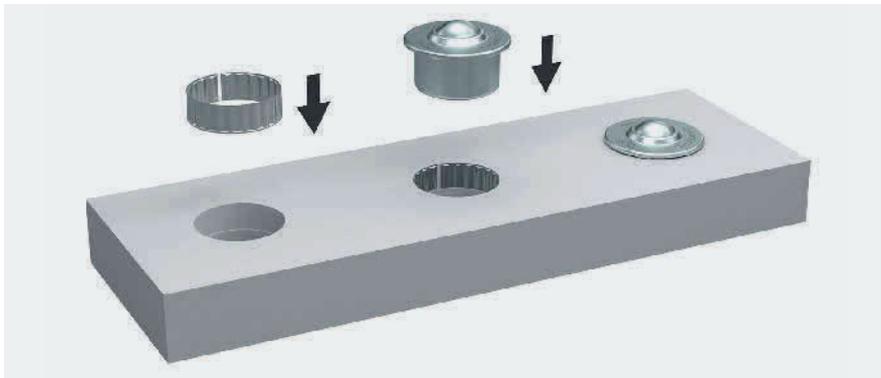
Montage einer Kugelrolle mithilfe eines Toleranzrings. Foto: Bosch Rexroth AG
